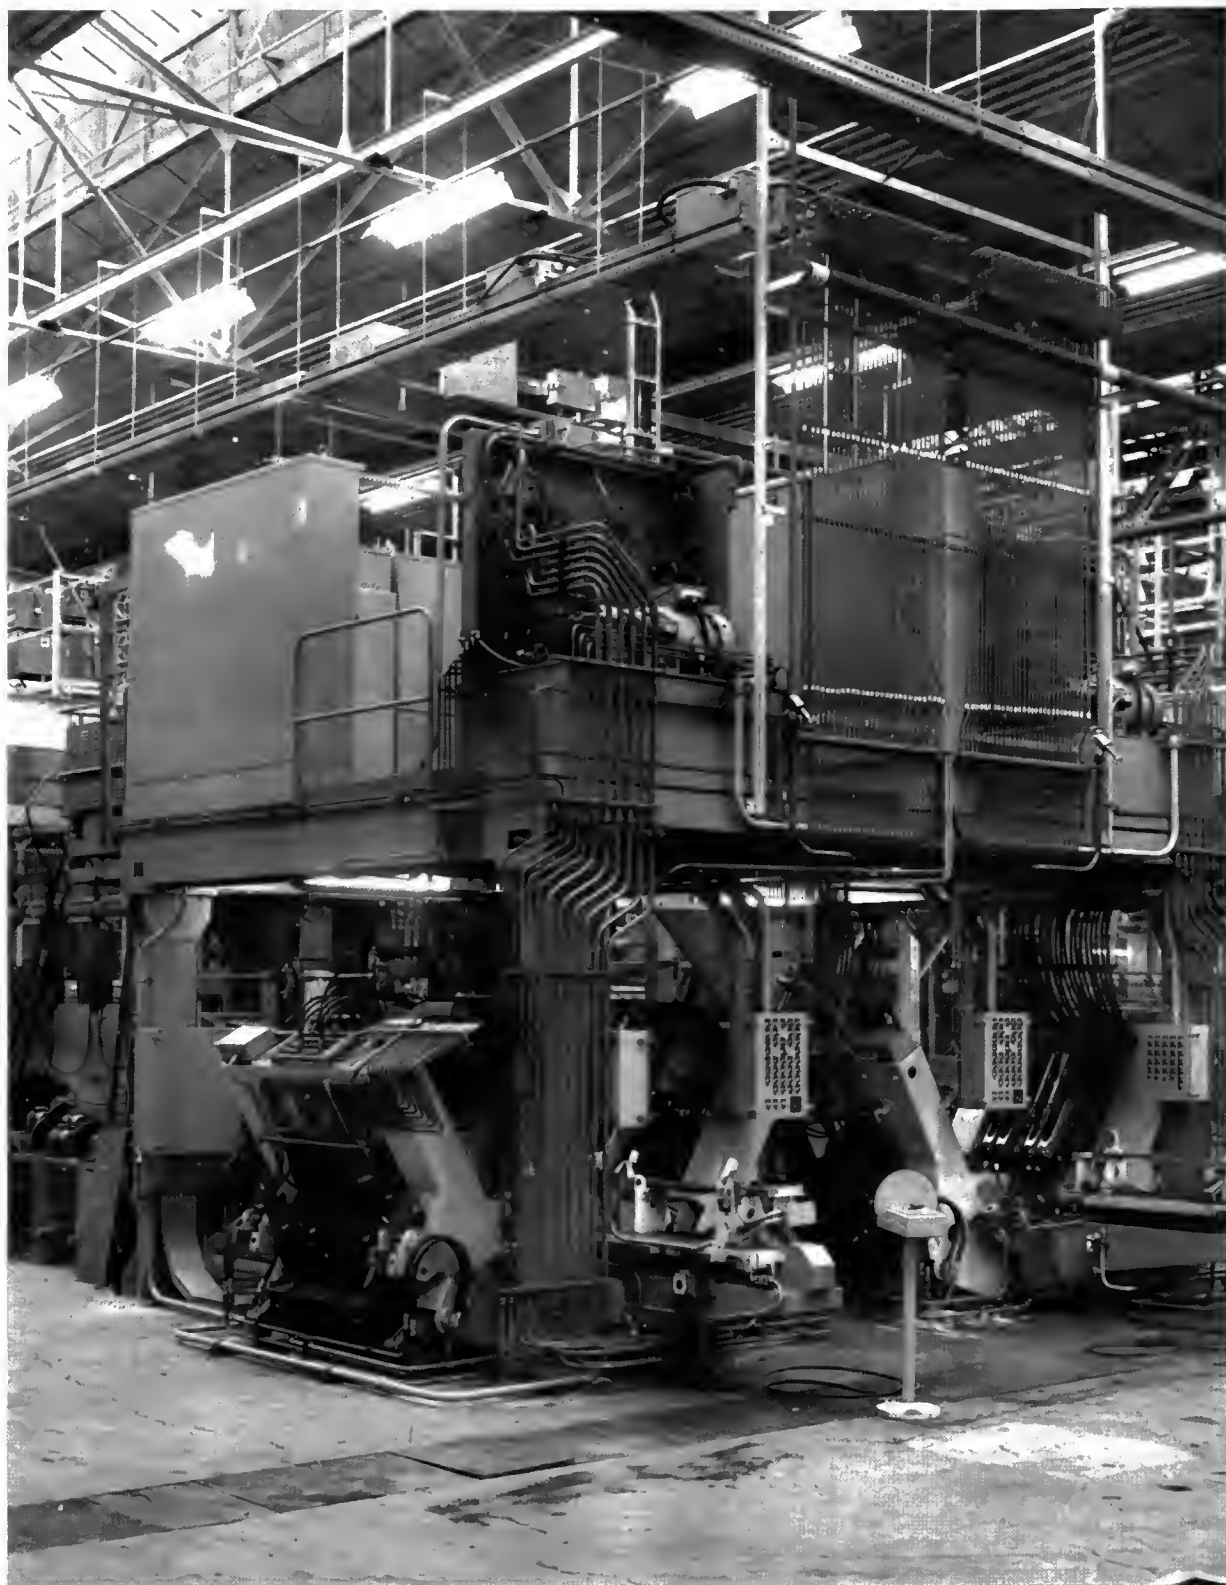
Machines automatiques pour soudage par points de traverses de suspension (tôles 3 + 3 mm, effort de 1 200 daN, 20 000 A, cadence de 70 pièces/heure par machine) (Peugeot)
